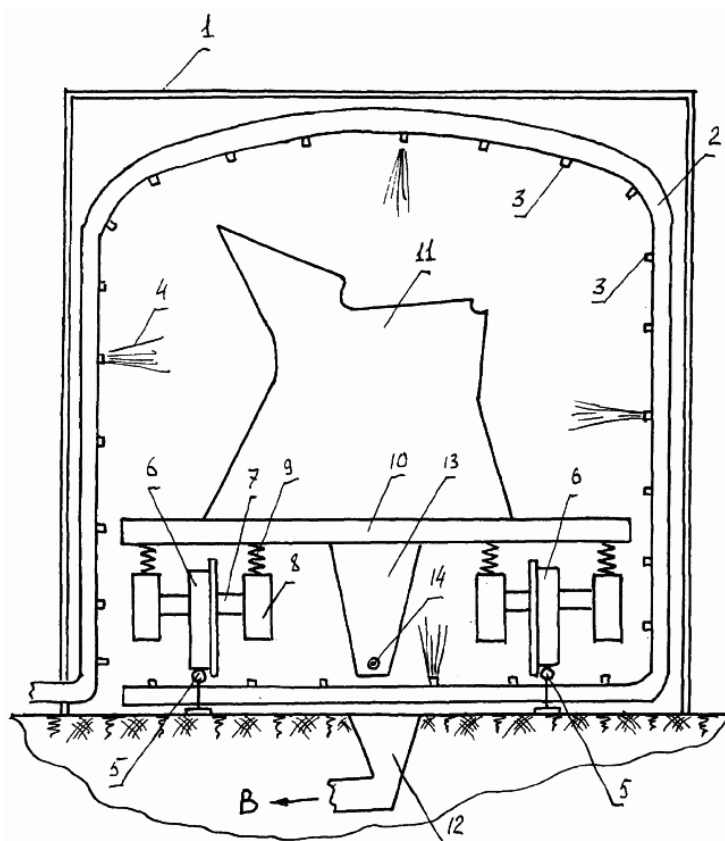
Установка для мойки деталей (патент РФ № 2267366)
